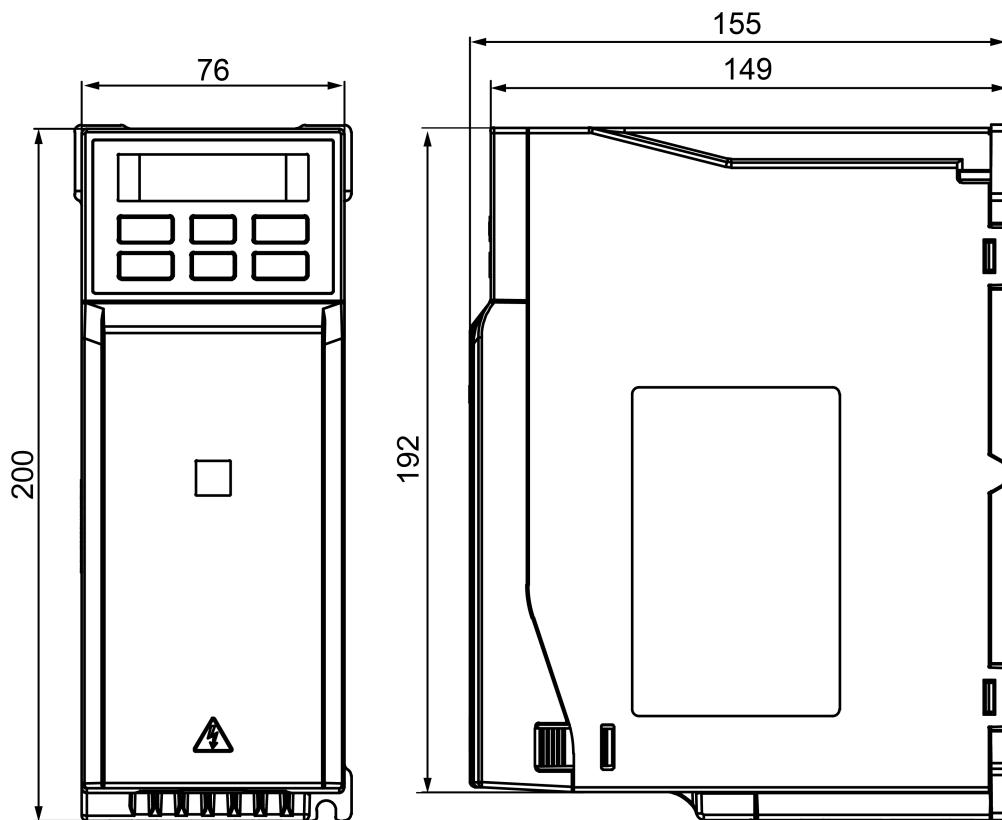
Габаритные размеры прибора в корпусе типоразмера 1
